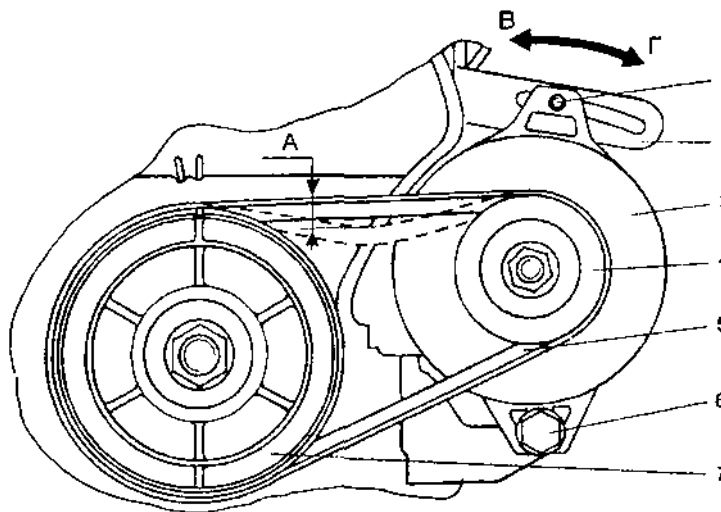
Привод генератора и проверка натяжения ремня: 1 - болт крепления генератора; 2 - планка натяжная; 3 - ремень; 4 - шкив привода генератора; 5 - генератор; 6 - болт крепления генератора к кронштейну; 7 - шкив коленчатого вала.
